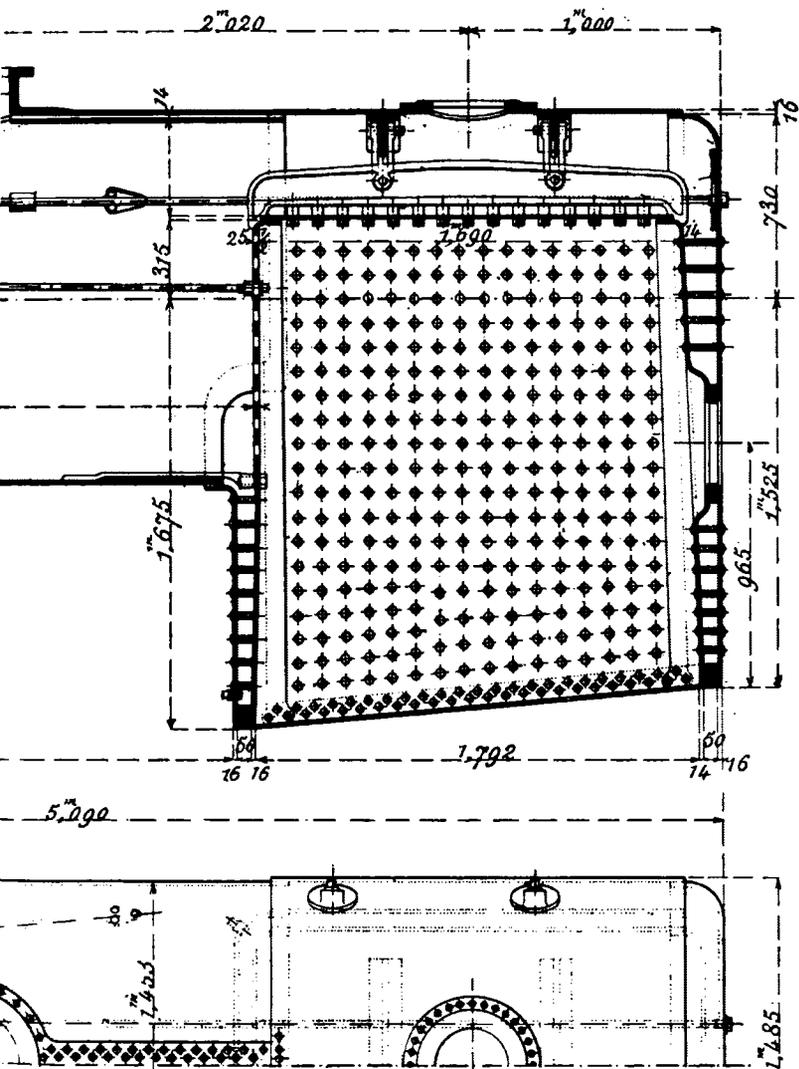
Type de chaudière à foyer Crampton; locomotives
